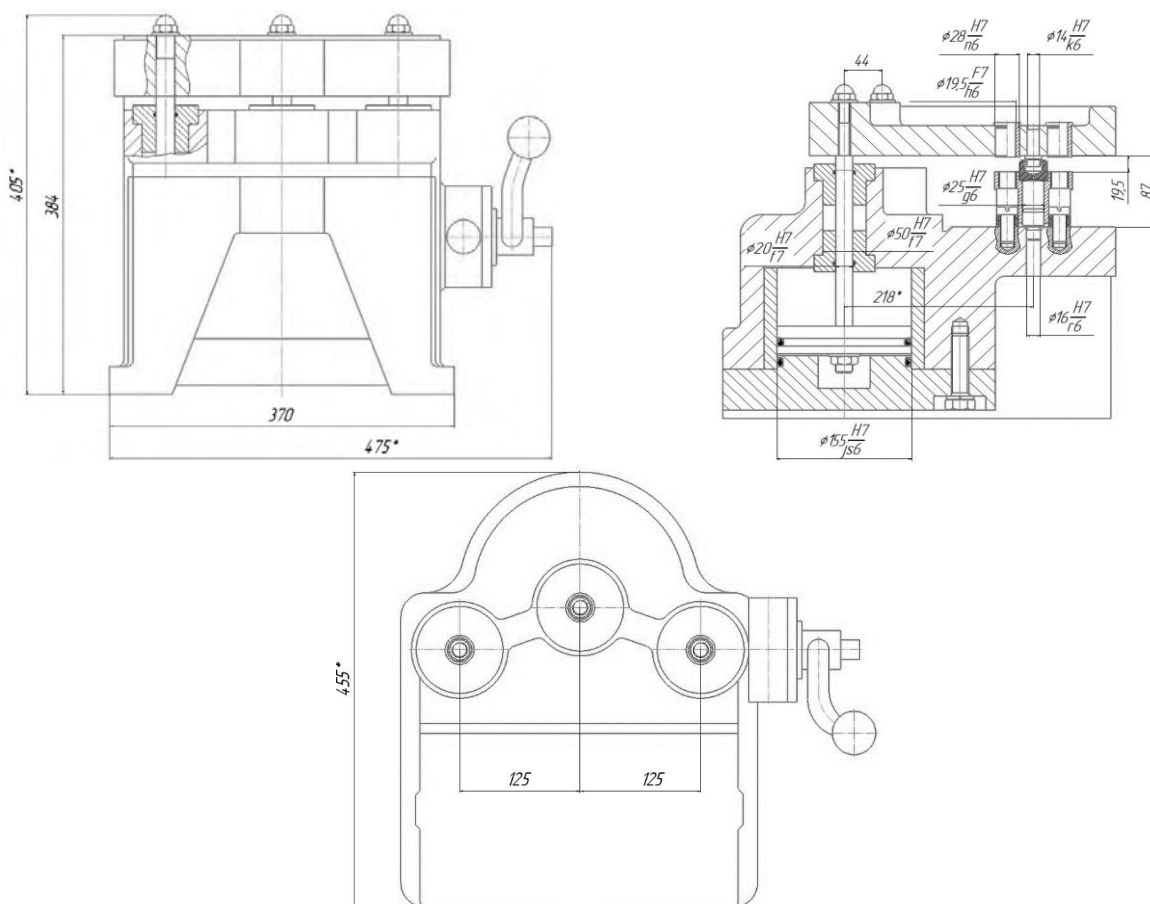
Чертеж скальчатого консольного кондуктора с пневматическим закреплением с установкой заготовки на цилиндрический палец и кольцевую опору
